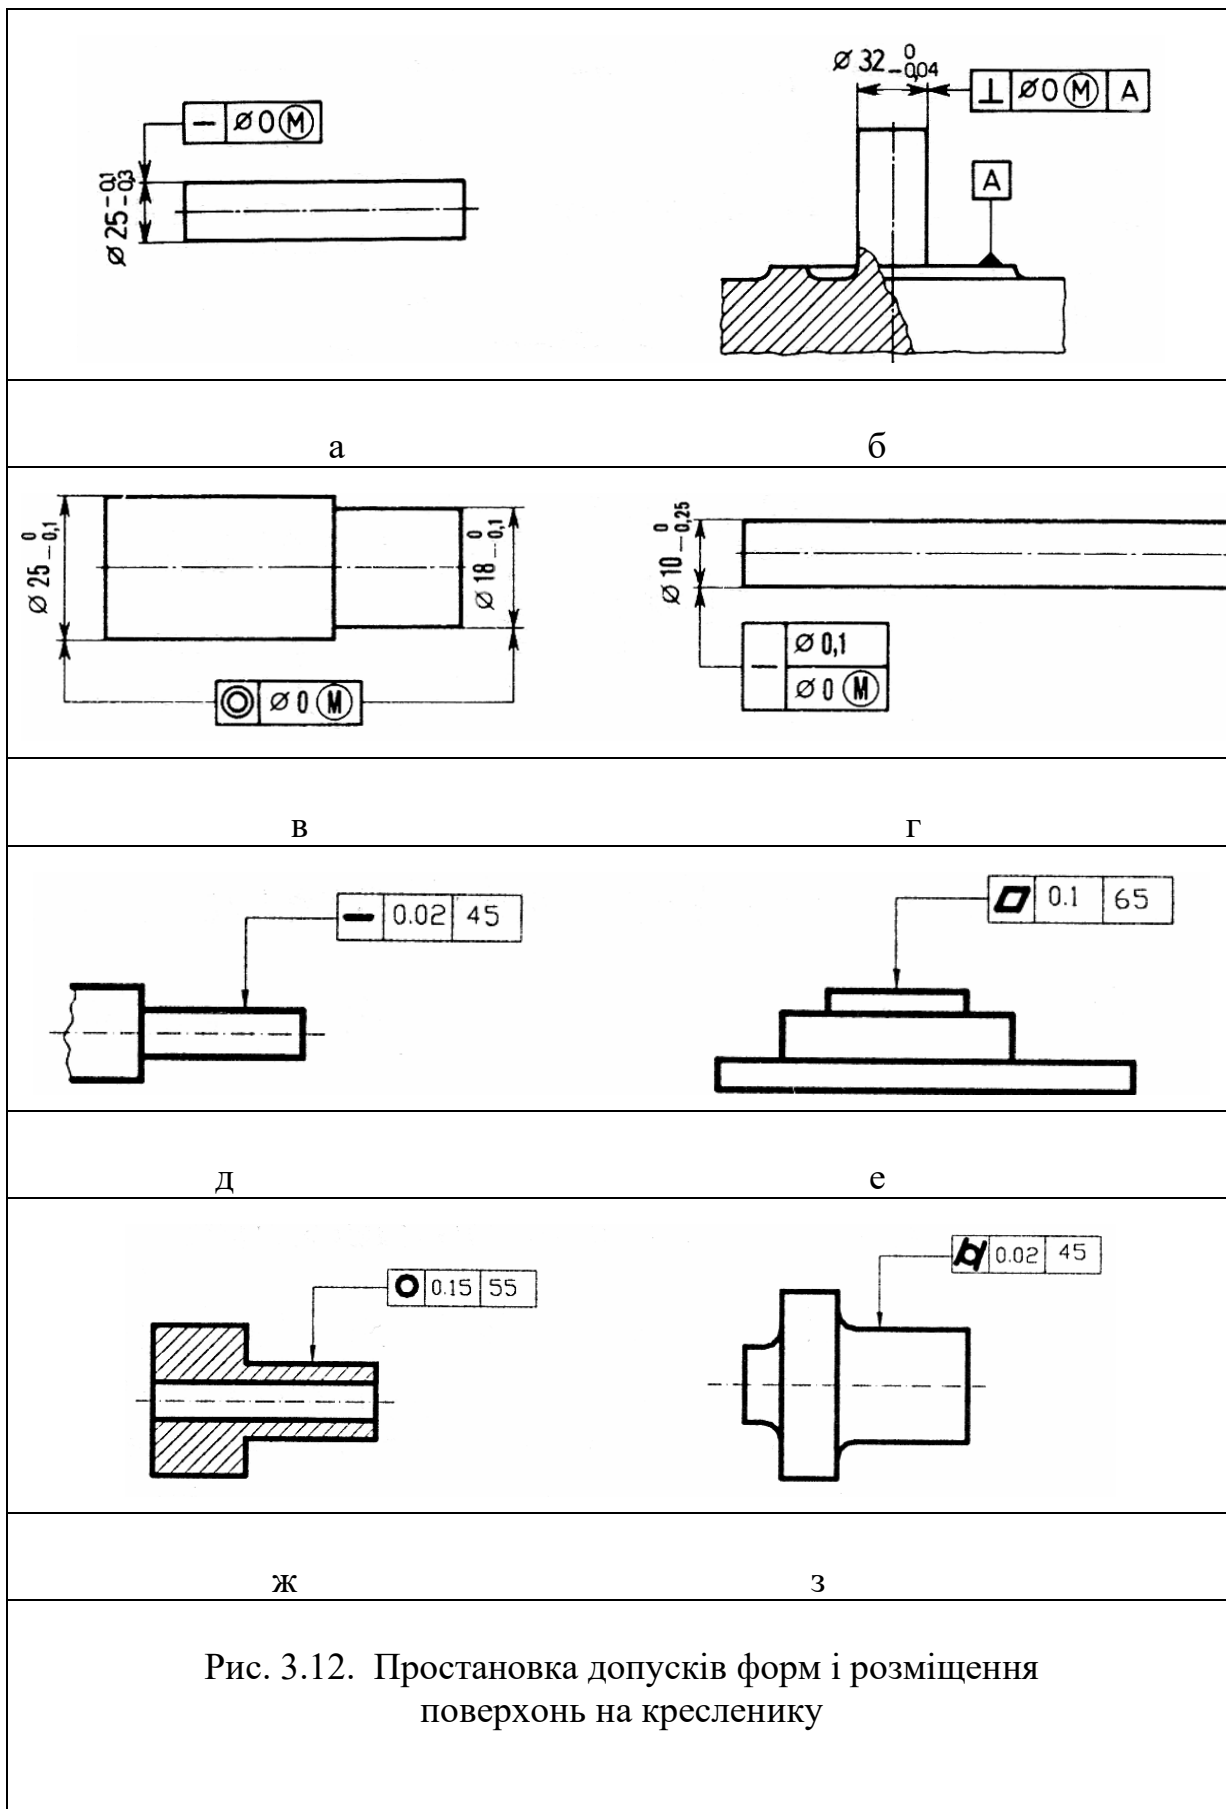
Простановка допусків форм і розміщення поверхонь на кресленіку
